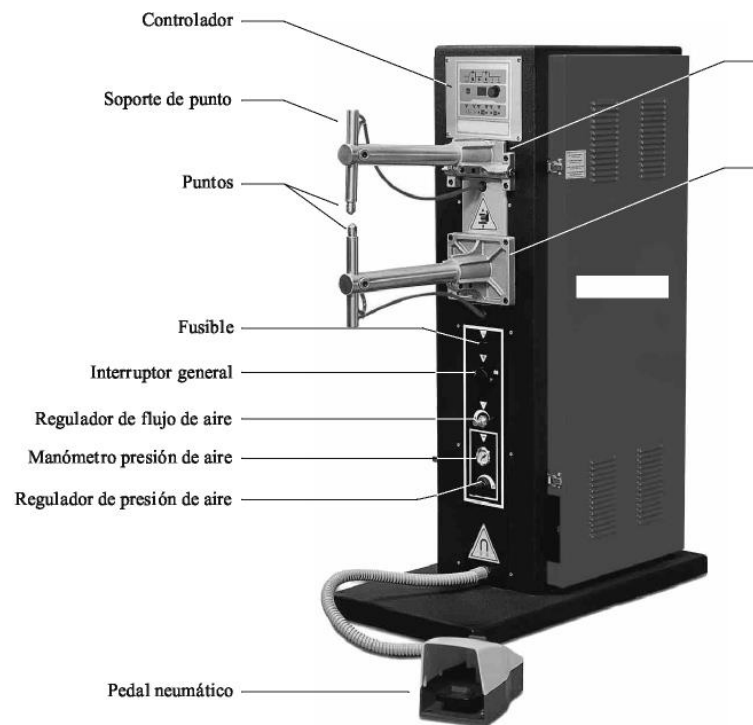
Equipo de soldadura "MPH Digital Neumática"
